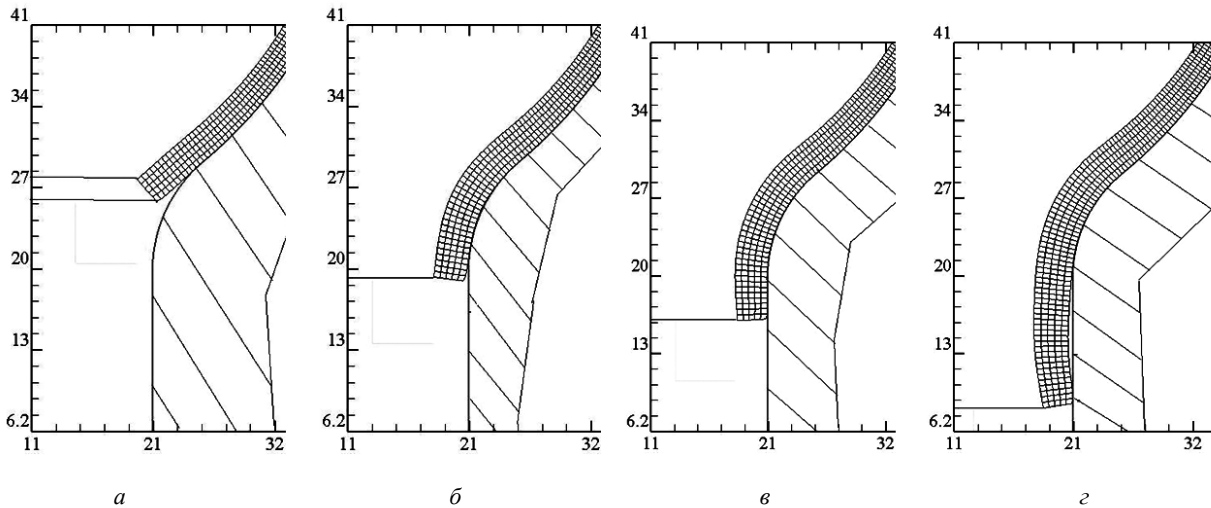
Послідовність формоутворення горловини при обтиску трубчатой заготовки в сферичній матриці (розміри приведені в міліметрах)
